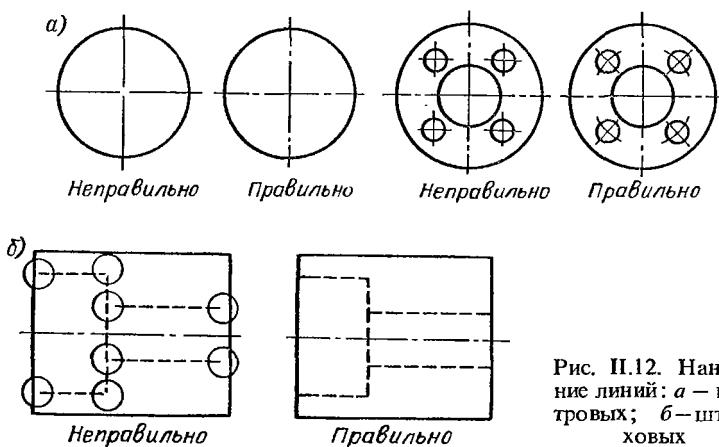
Нанесение линий: а — центровых; б — штриховых
